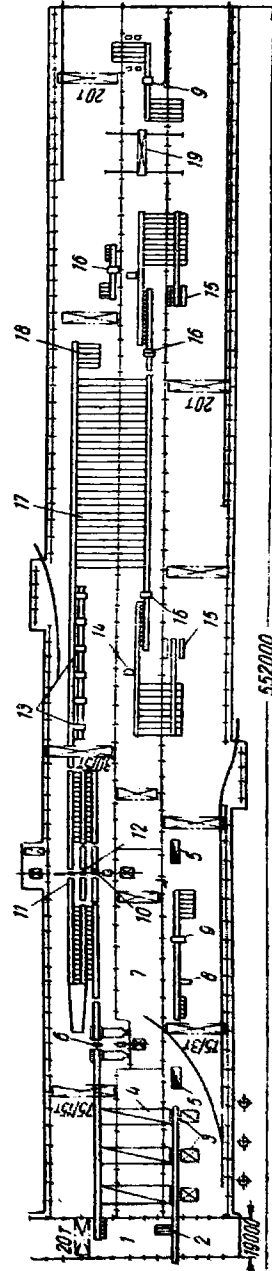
Схема расположения оборудования крупносортового стана 650:
